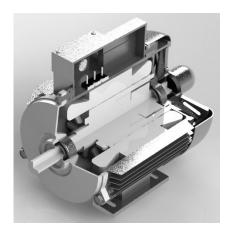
Внешний вид энергоэффективного двигателя улучшенной конструкции
